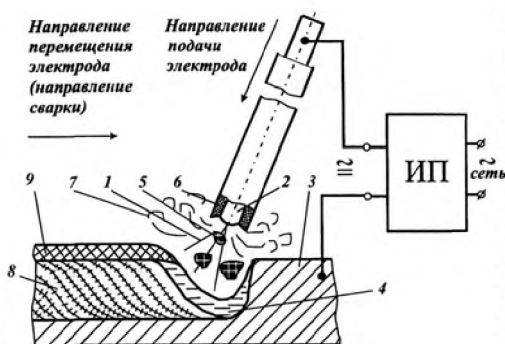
Схема ручной дуговой сварки покрытыми электродами; ИП – источник питания
